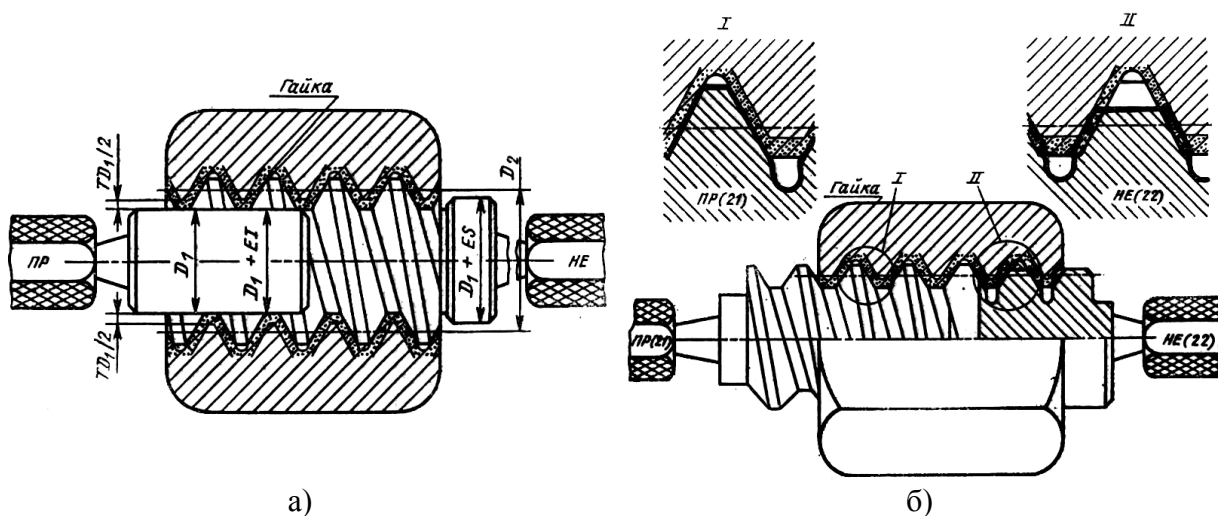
Гладкие калибры-пробки (а) и резьбовые калибры-пробки (б) для контроля внутренней резьбы
